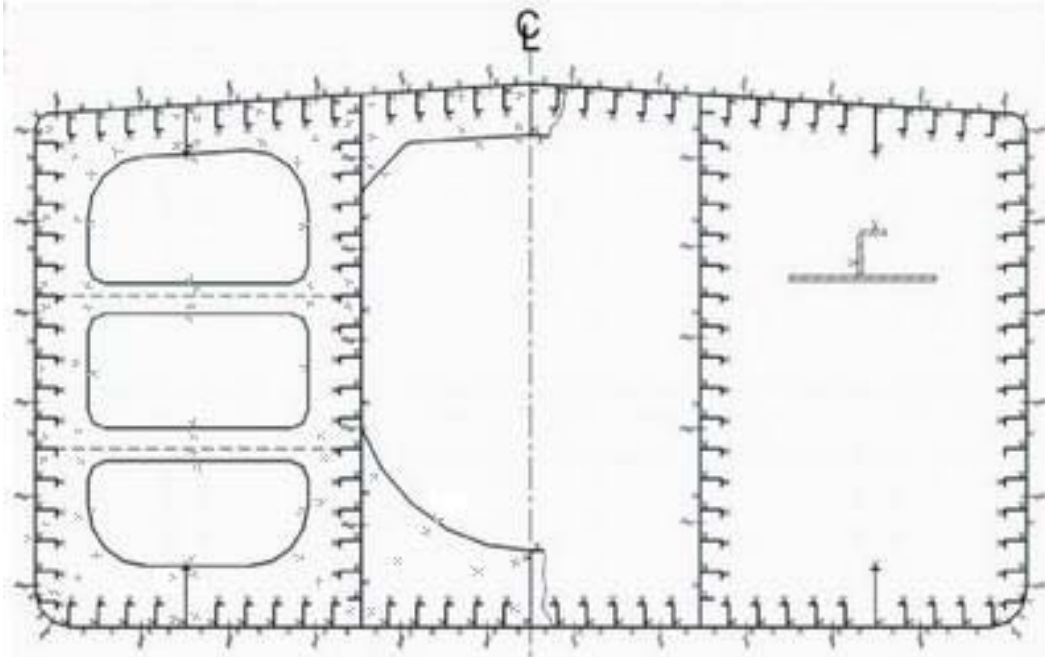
Схема замеров элементов корпуса в поперечном сечении однокорпусного нефтеналивного судна
